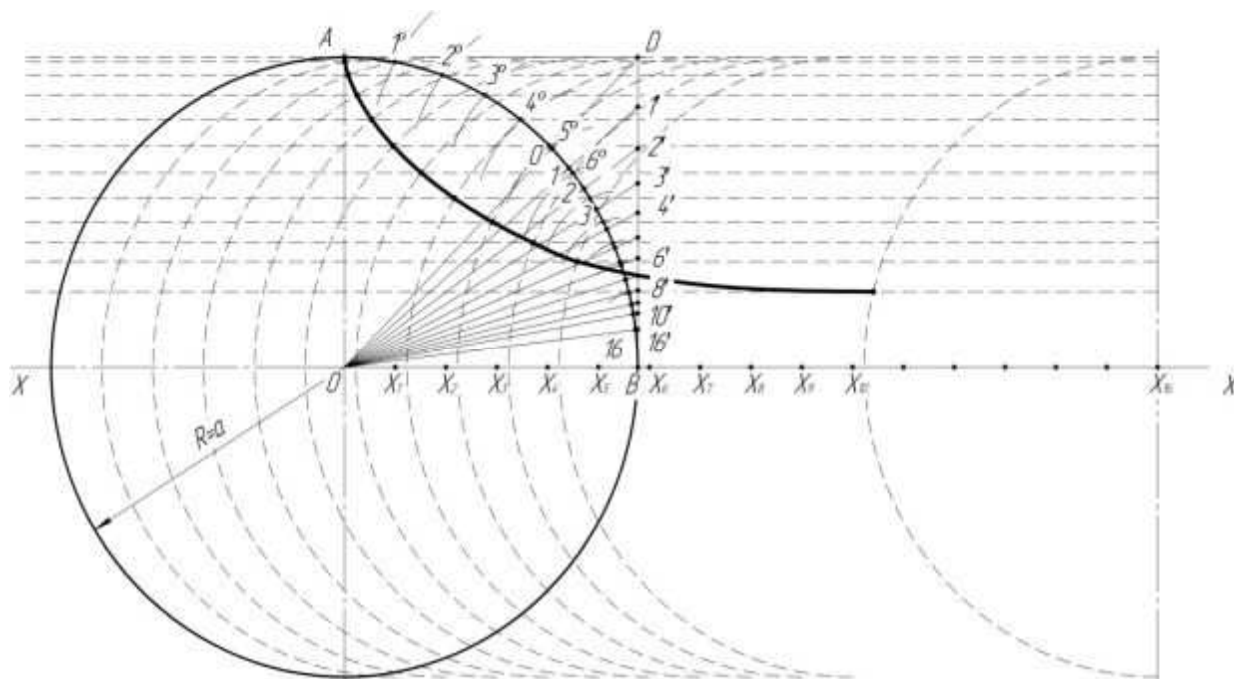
Построение профиля поверхности рабочего канала формовочной головки пресса
